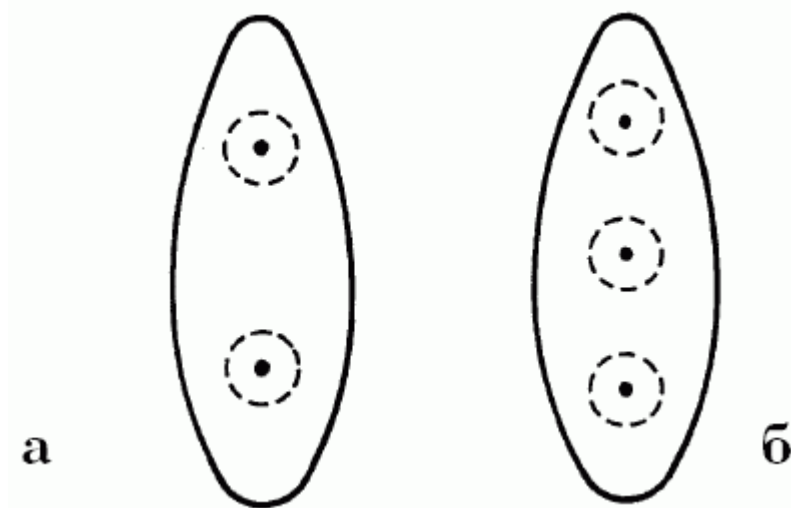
Точечная электроконтактная сварка – места сварки в составных блеснах
